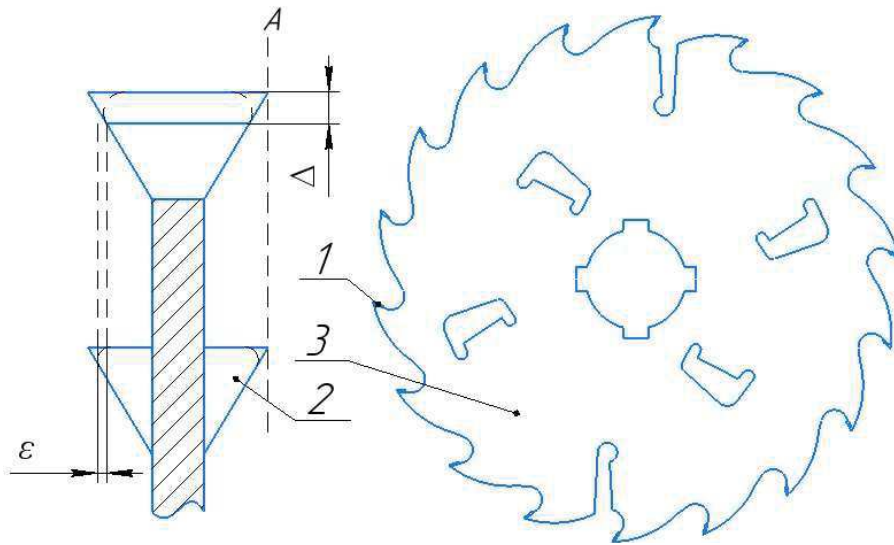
Схема плоскости движения зуба пилы и стабилизатора
